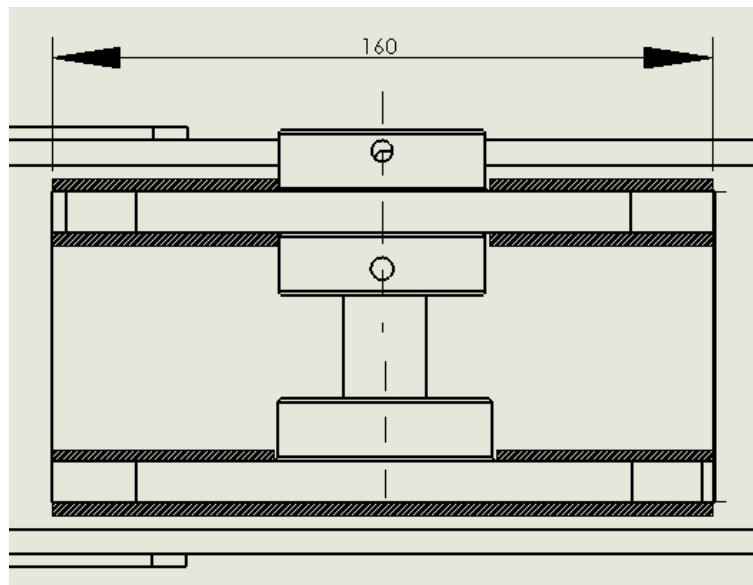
Vista superior de los cordones de soldadura.
